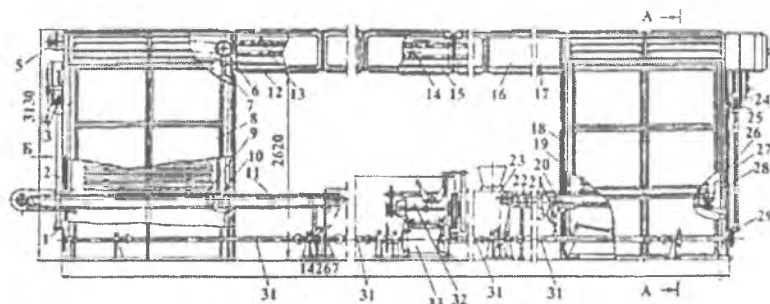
Установка К-52Д ускоренной выстойки корпусов конфет шахтного типа
